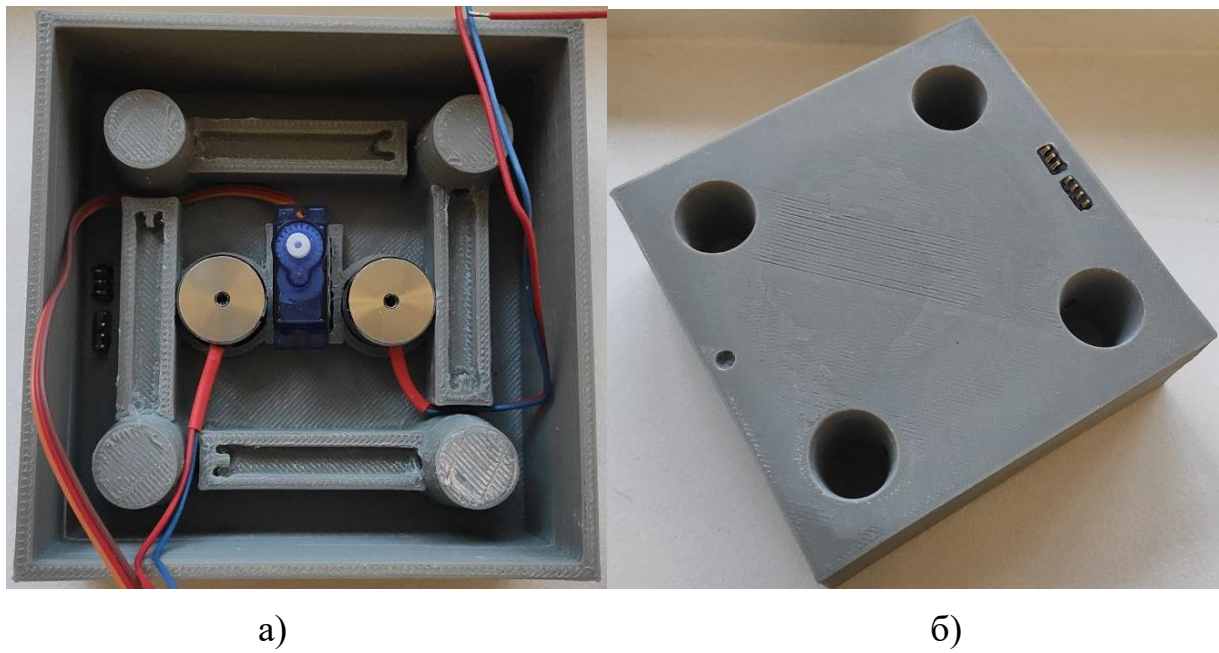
Базова поверхня для встановлення інструменту вигляд: а) зверху;
